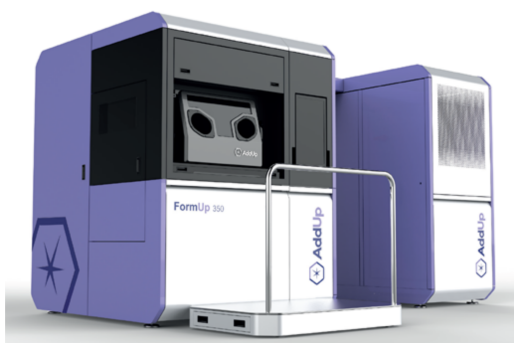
Machine de fabrication additive par fusion laser sur lit de poudre
